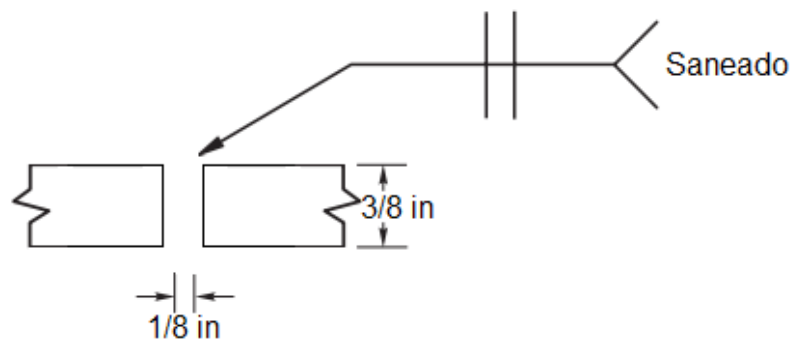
Diseño de unión de los cupones de soldadura.
